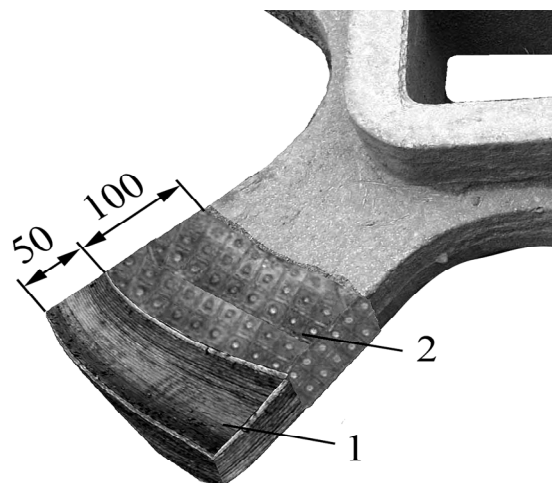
Схема наплавки звездочек порошковой проволокой Ледурит-68
